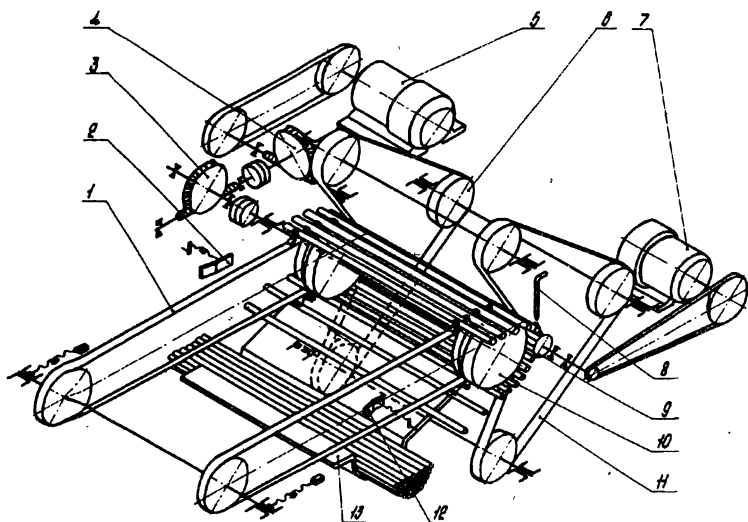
Кинематическая схема станка для подрезки трубчатого пороха.
